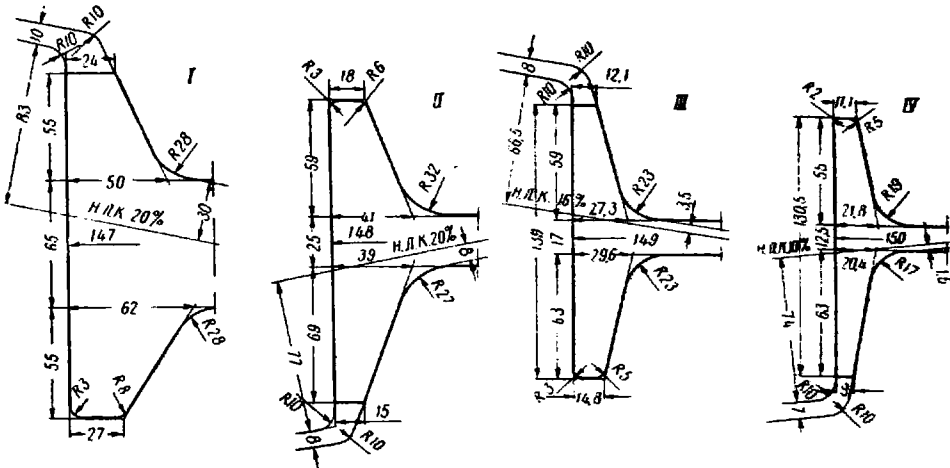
Косорасположенные калибры для прокатки балки № 16
